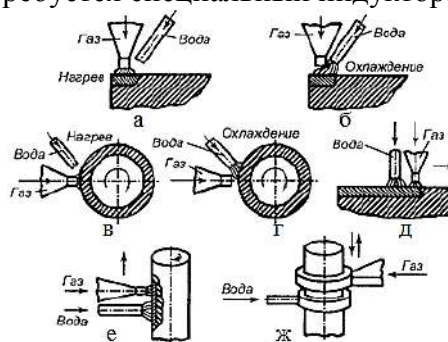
Схемы поверхностной заковки деталей с нагревом газовым пламенем: а-г-циклическим способом; д-ж - непрерывно-последовательным способом
